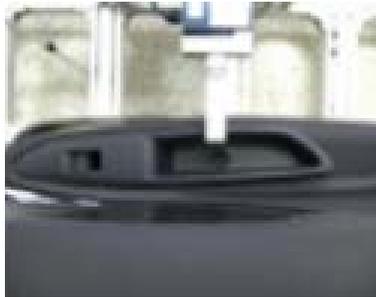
Pruebas físicas –Prueba de fatiga - switch plate.
